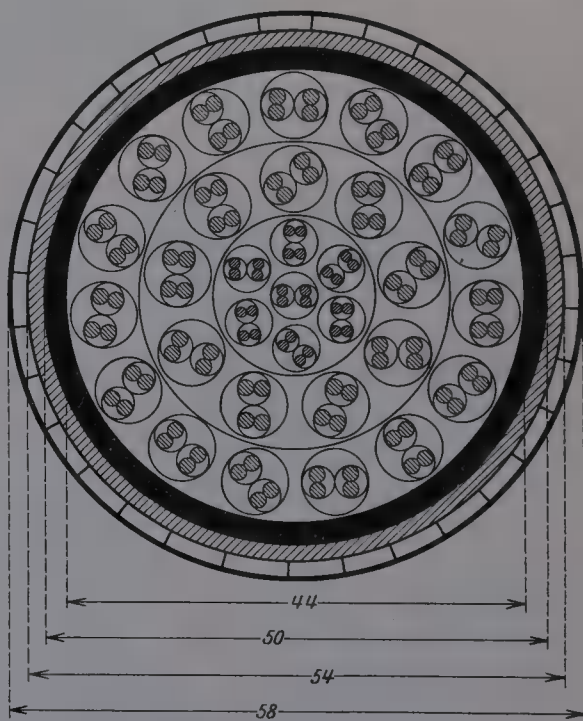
Schweizerisches Normal-Fern-Telephonkabel mit 62 Adernpaaren. (OTD.)
